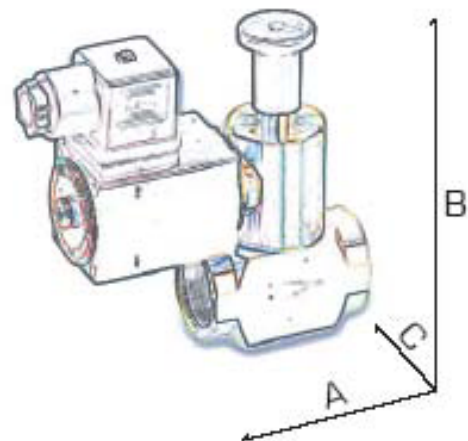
Габаритные размеры клапана (одинаковые для версий 500мБар и 6Бар)
